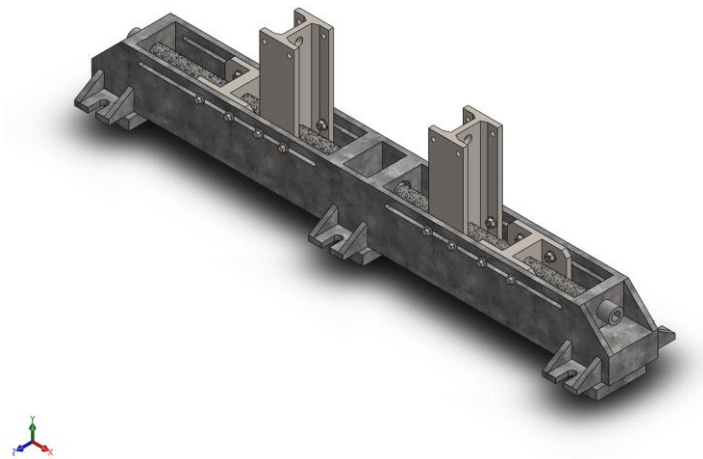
Montaje preliminar del soporte de motor y la viga de soporte.
